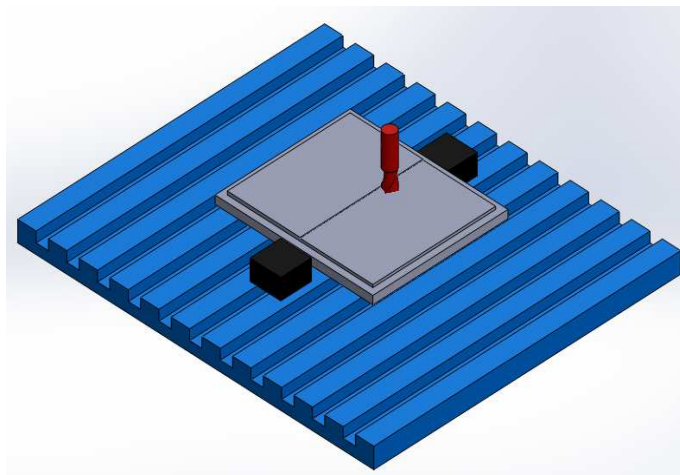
Maquinagem da superfície em contacto com os provetes.
